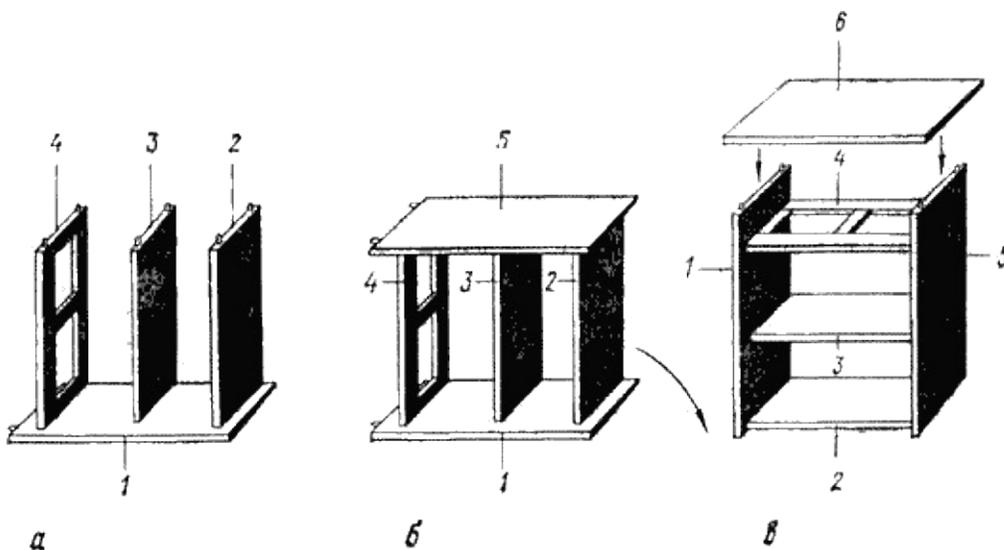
Сборка разделочного стола-шкафа: а — присоединение днища, полки и подъящичной рамки к боковой стенке; б — присоединение второй боковой стенки; в — присоединение крышки; 1 — первая боковая стенка; 2 — днище; 3 — полка; 4 — подъящичная рамка; 5 — вторая боковая стенка; 6 — крышка
